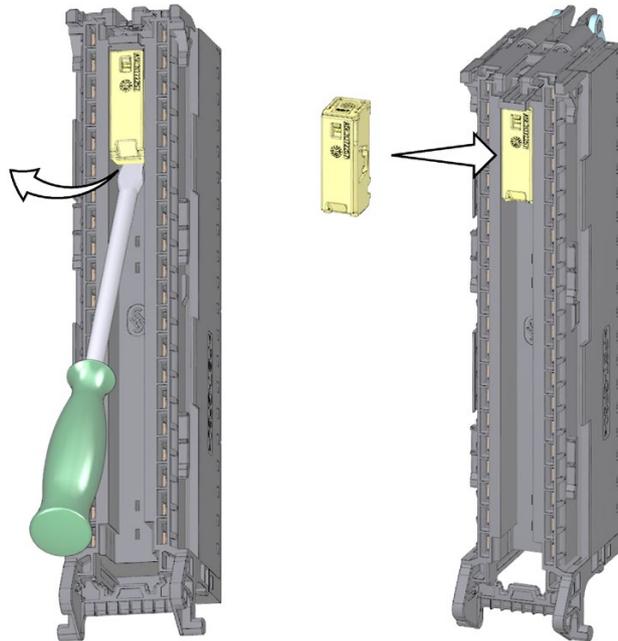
Desmontaje del elemento codificador electrónico del conector frontal y colocación en el conector frontal nuevo
